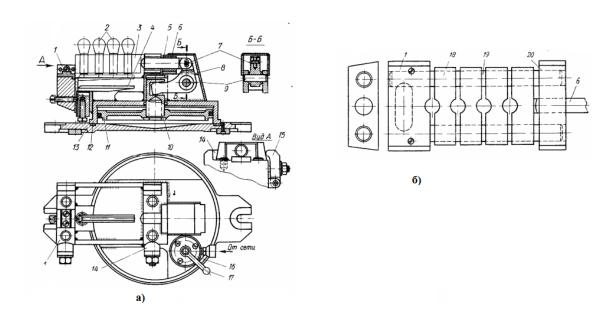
Универсальнгое приспособление: а) общий вид приспособления, б) сменная наладка
